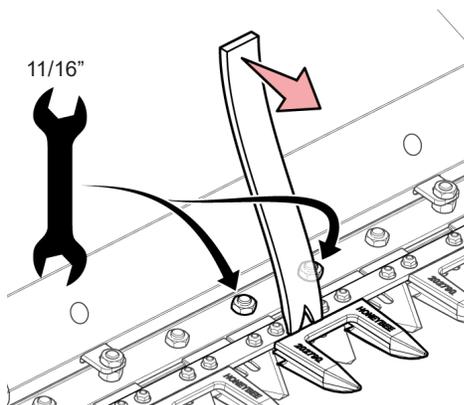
Fare leva sulla protezione in avanti durante il serraggio
